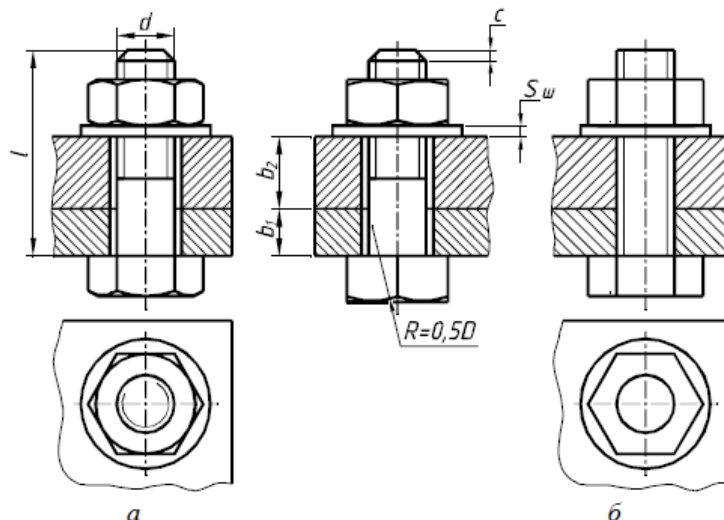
Болтове з'єднання; a – повне зображення, b – спрощене зображення
